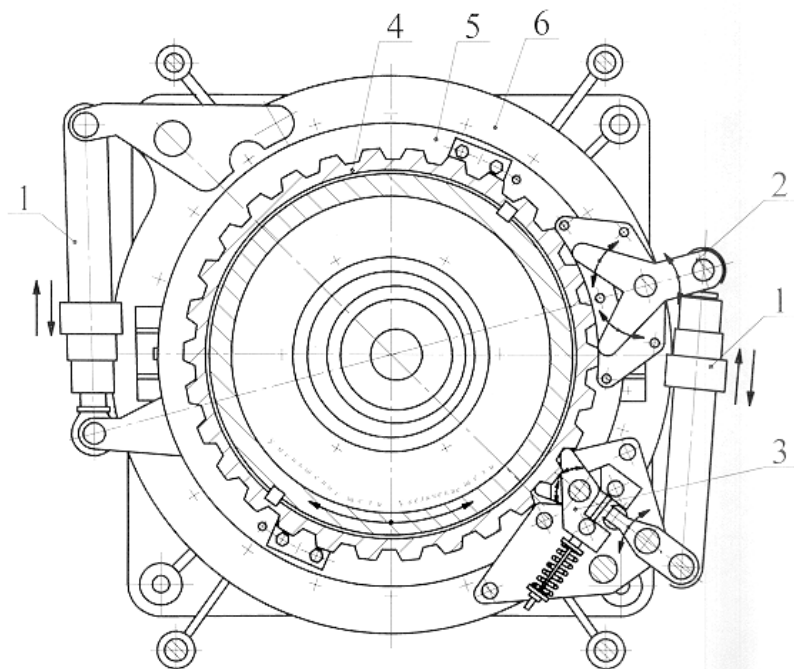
Схема регулировочного механизма конусной дробилки КСД-600
